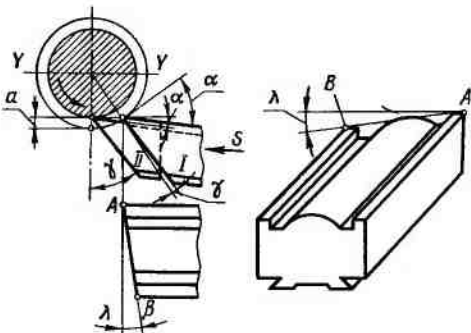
Обработка заготовки фасонным призматическим тангенциальным резцом
